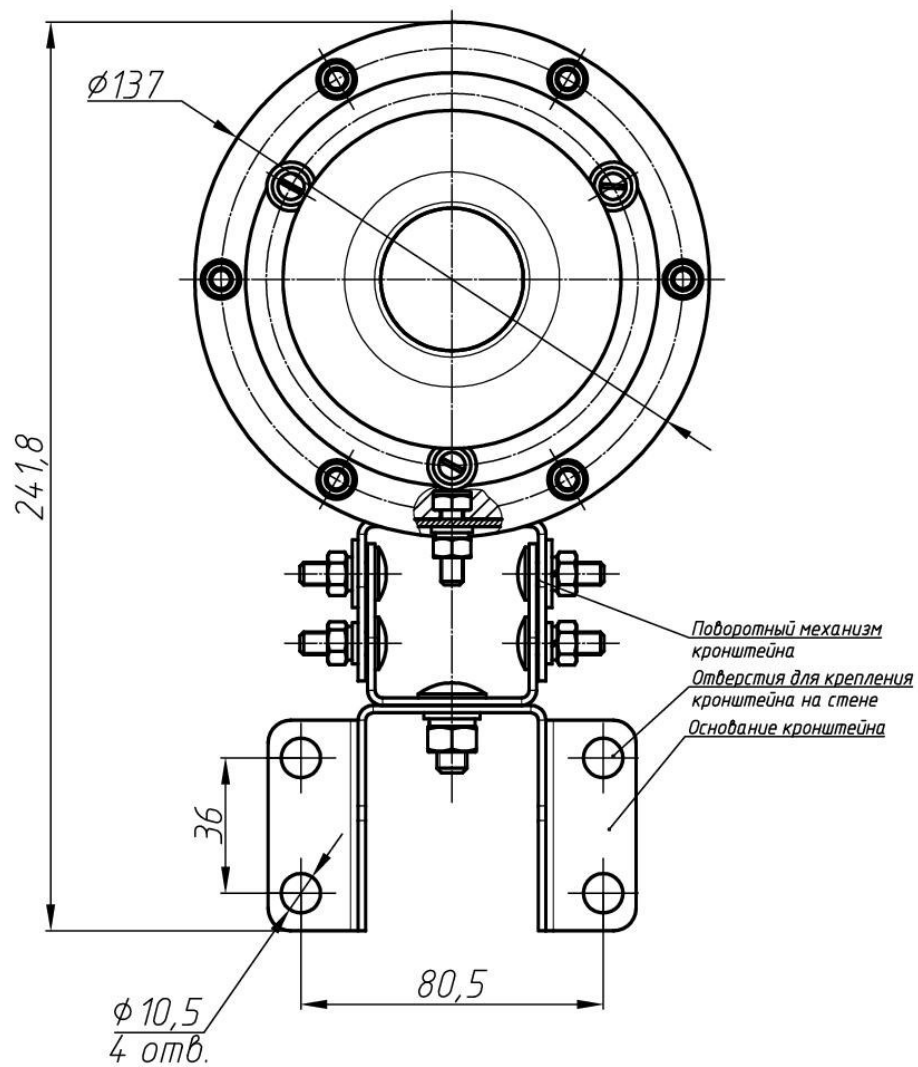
б - Габаритный чертёж оповещателя Рупор-В (вид спереди, без колокола).
